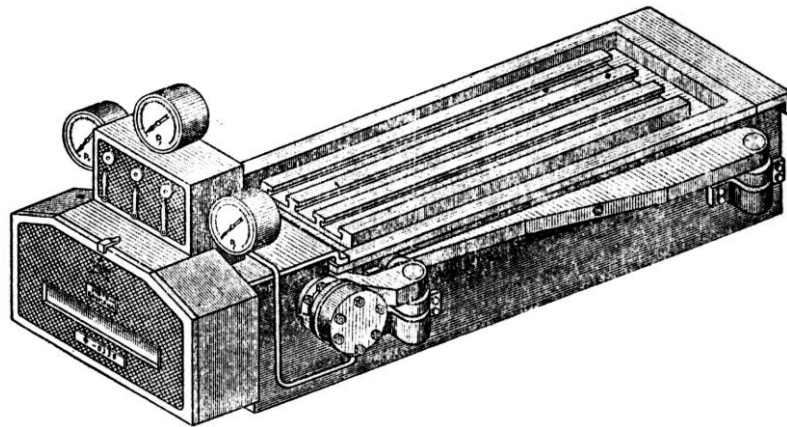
Фрезерний трьохкомпонентний динамометр
